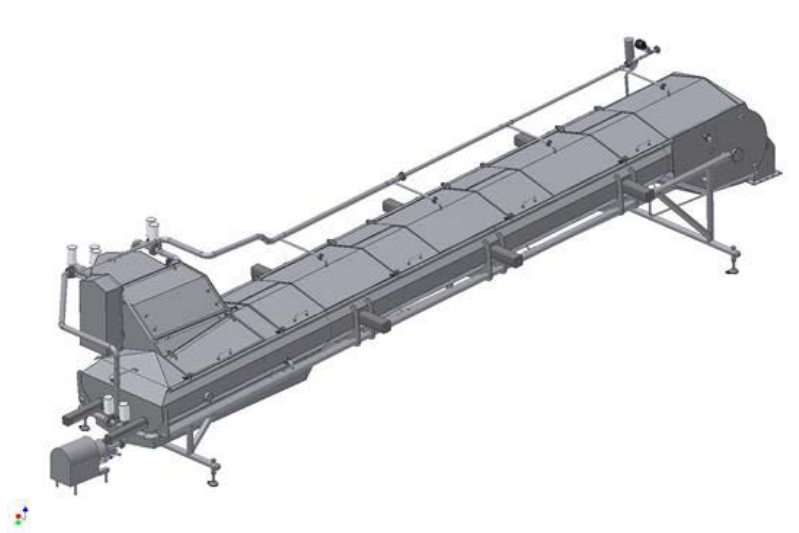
Внешний вид пресса для творога тип Р/Т
